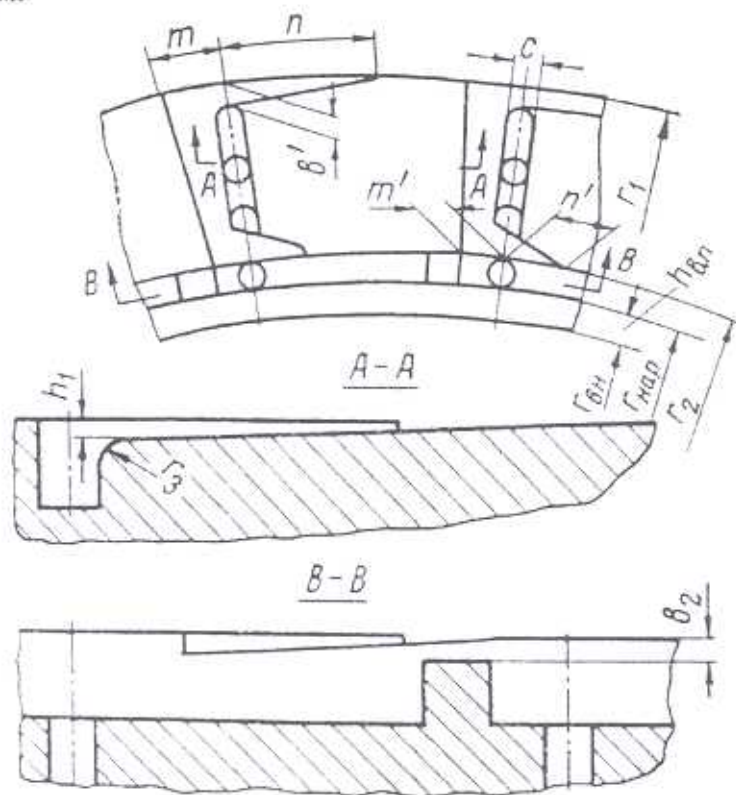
Форма разделки рабочей поверхности вкладыша [1]
